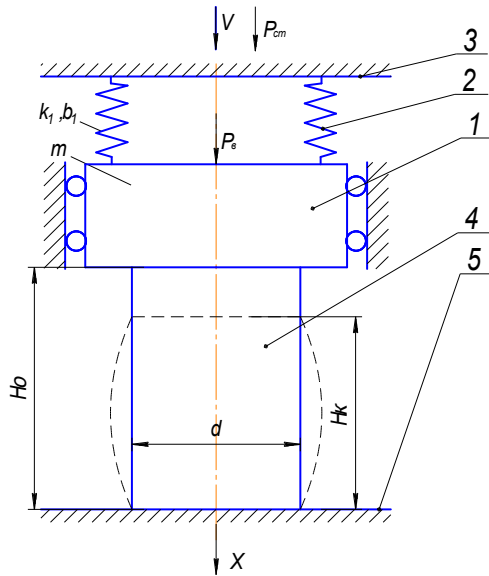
Расчетная схема осадки цилиндрической заготовки вибрирующим пуансоном прессы: 1 – пуансон; 2 – пружина; 3 – нажимная плита; 4 – заготовка; 5 – наковальня
